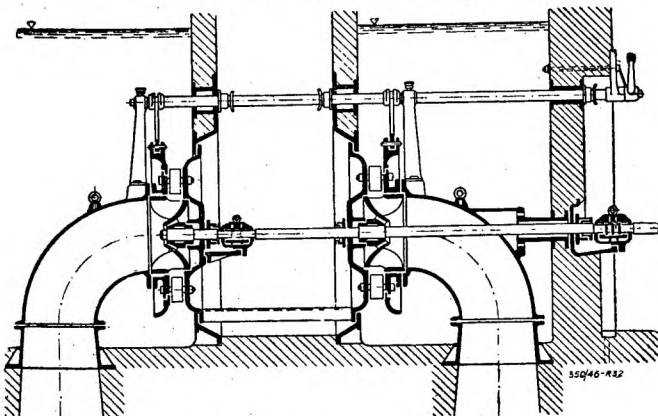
Wirniki turbiny śmigłowej Kaplana o mastawialnych łopatkach.
